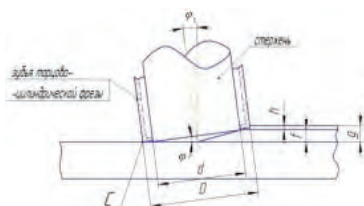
Схема обработки сварного шва методом РПД
